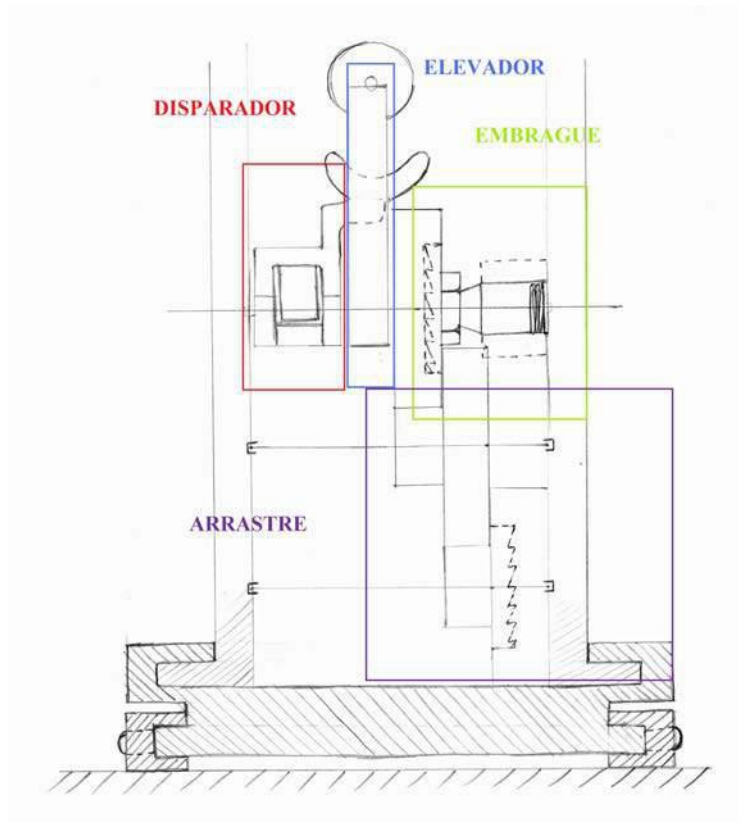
Dibujo de la posible distribución en planta de los elementos del mecanismo.
